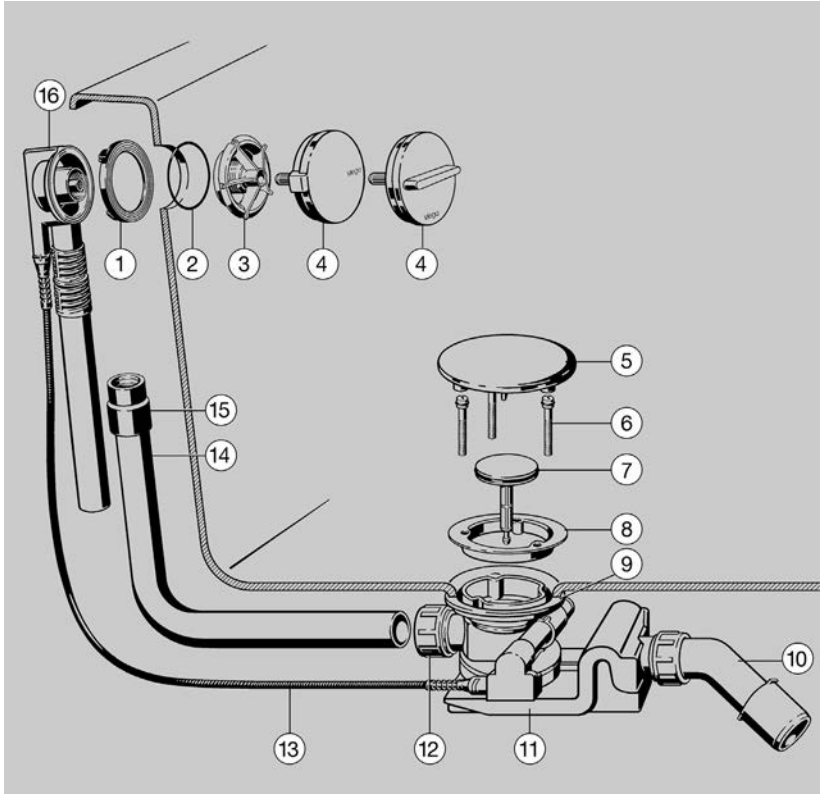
65 Componentes – Rotaplex Visign R5/R3
